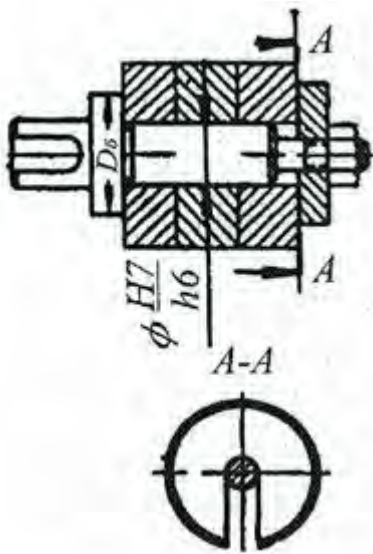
Установка заготовок на жорсткій оправці (посадка з зазором)
